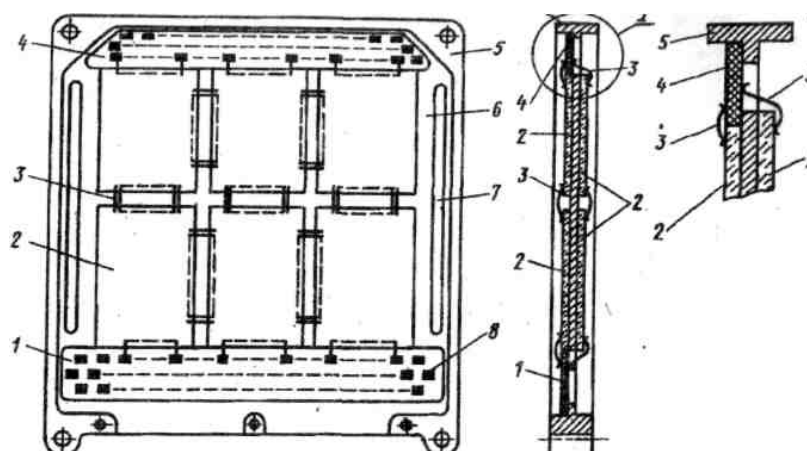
Конструкция двухсторонней ФЯ на металлической рамке:
